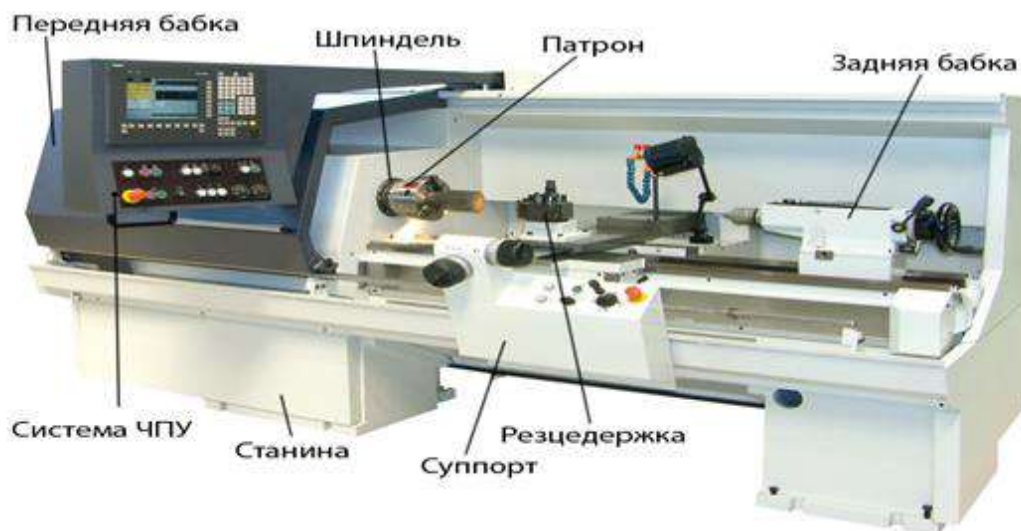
Современный универсальный станок с ЧПУ
